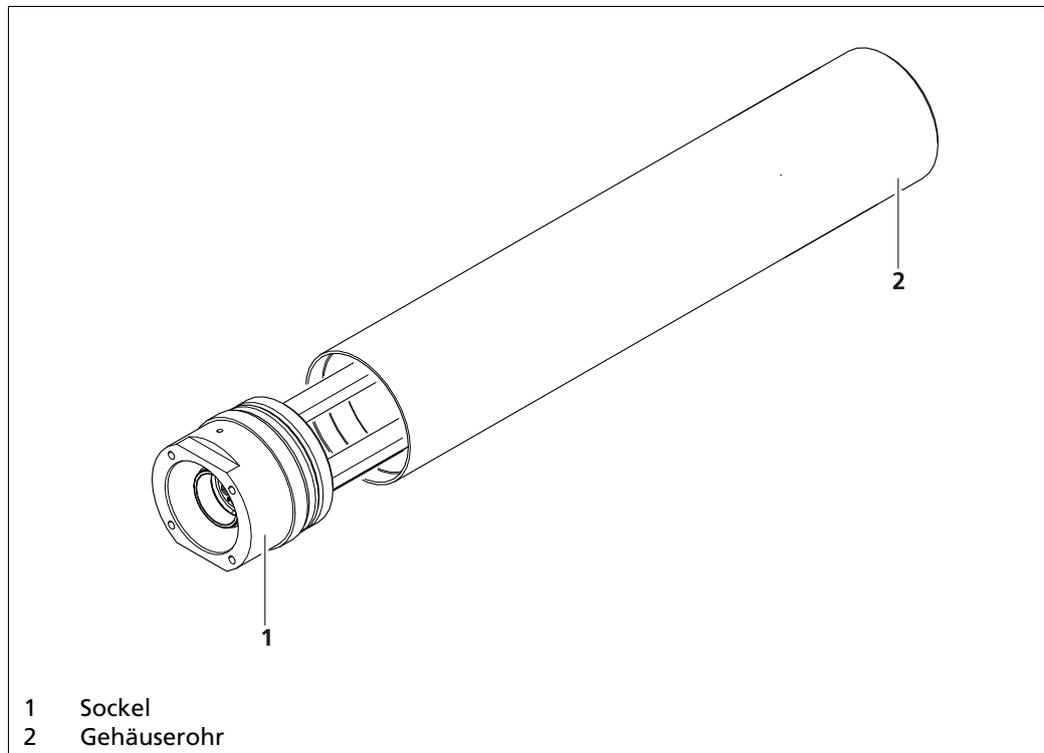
GAMMAcast-Detektor LB 6760, mit Gehäuserohr
